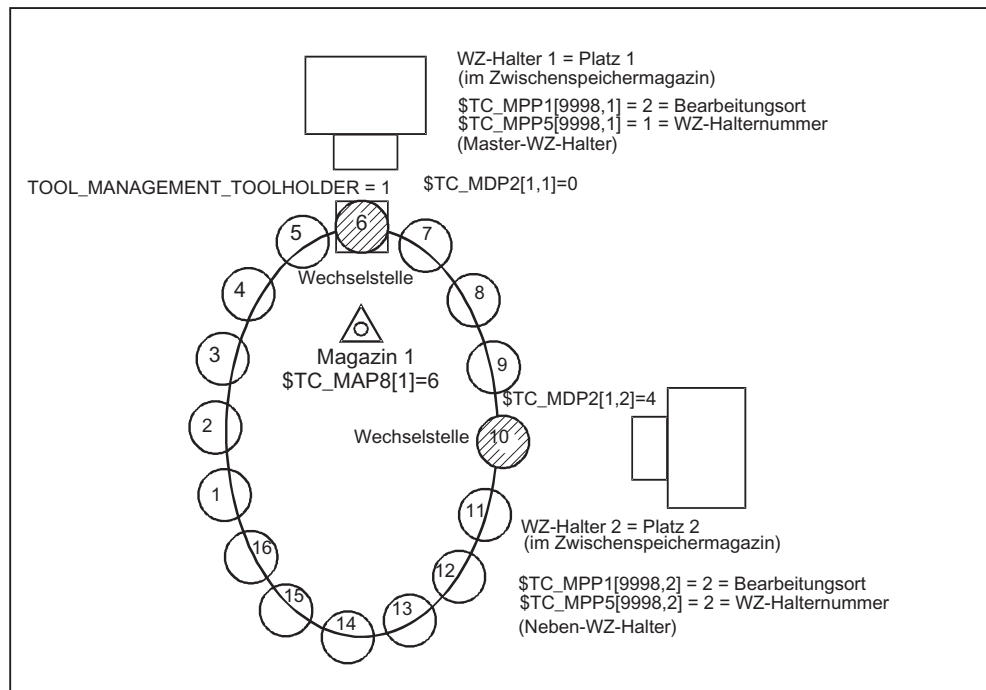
1 Kanal mit 2 Werkzeughaltern
